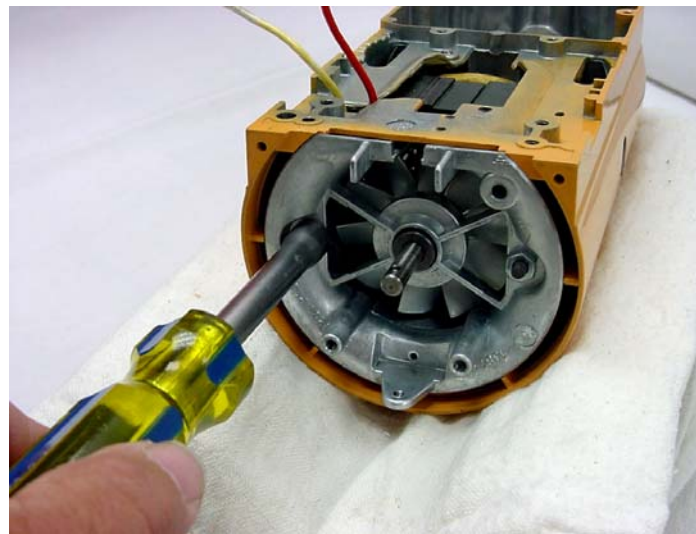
Zwei #10-24-Muttern von der Lagerbrücke entfernen.
